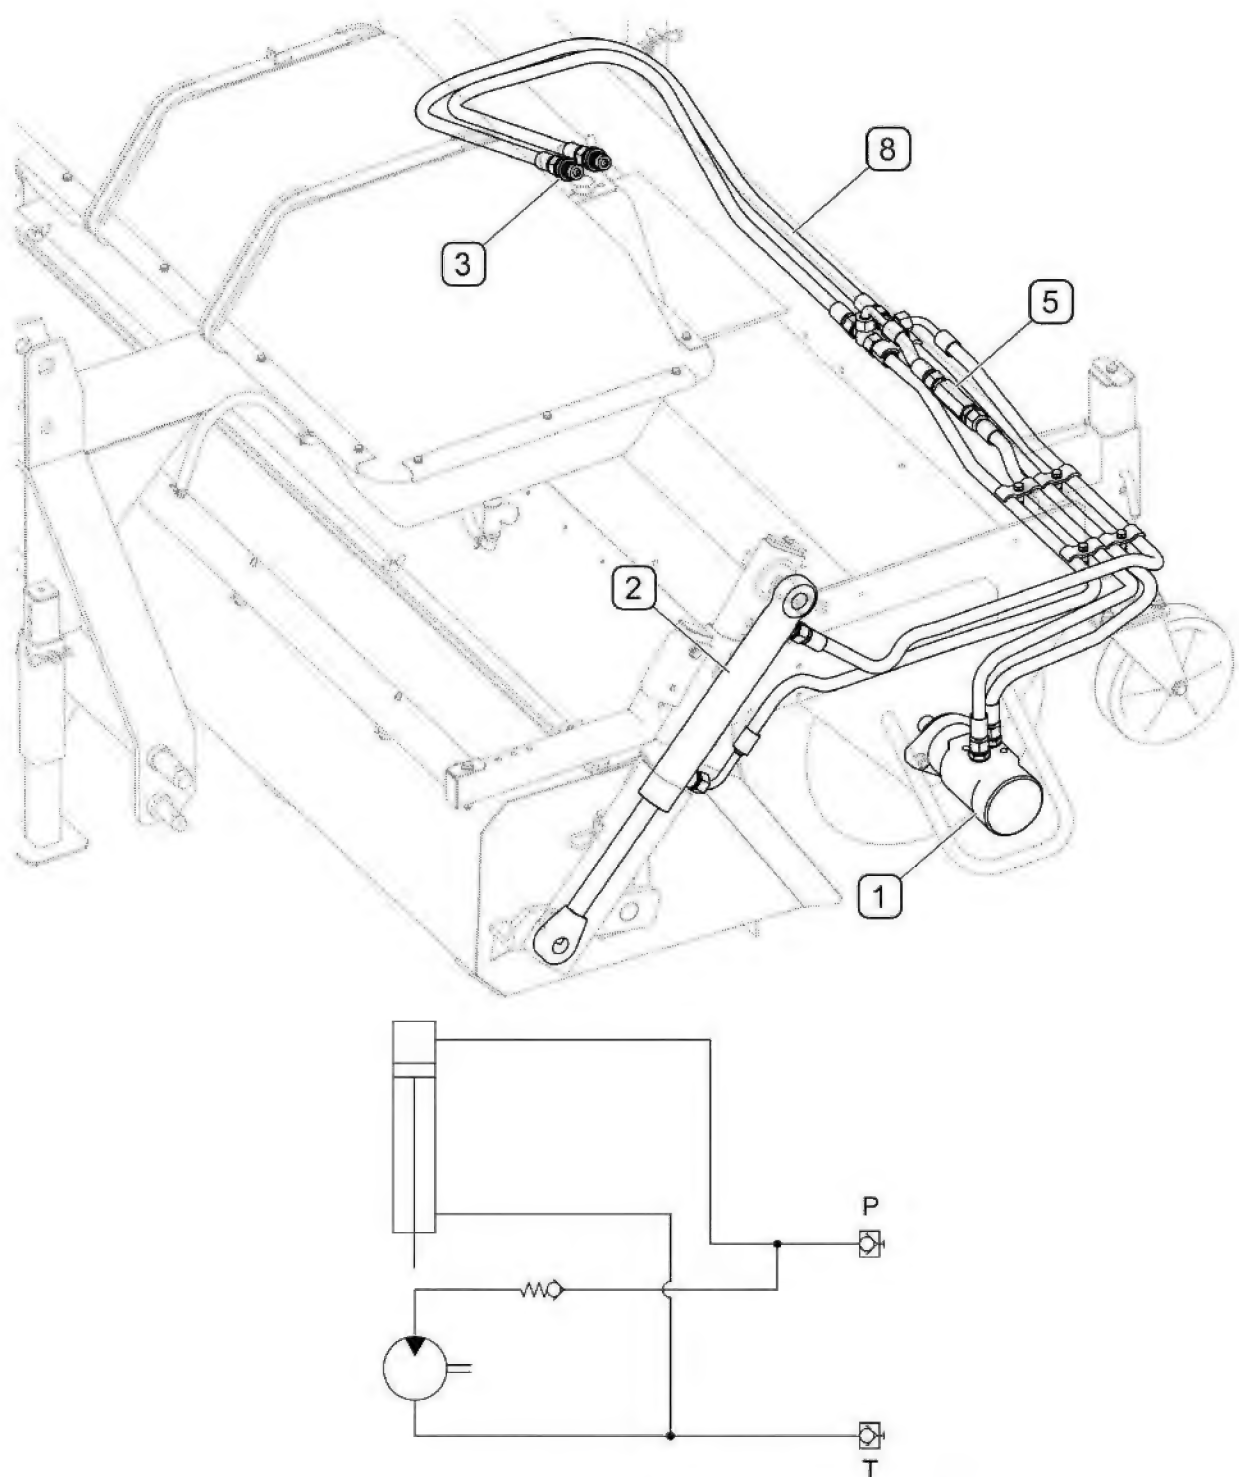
A Construction du circuit hydraulique des balayeuses ZM-1600 et ZM-1600-02
